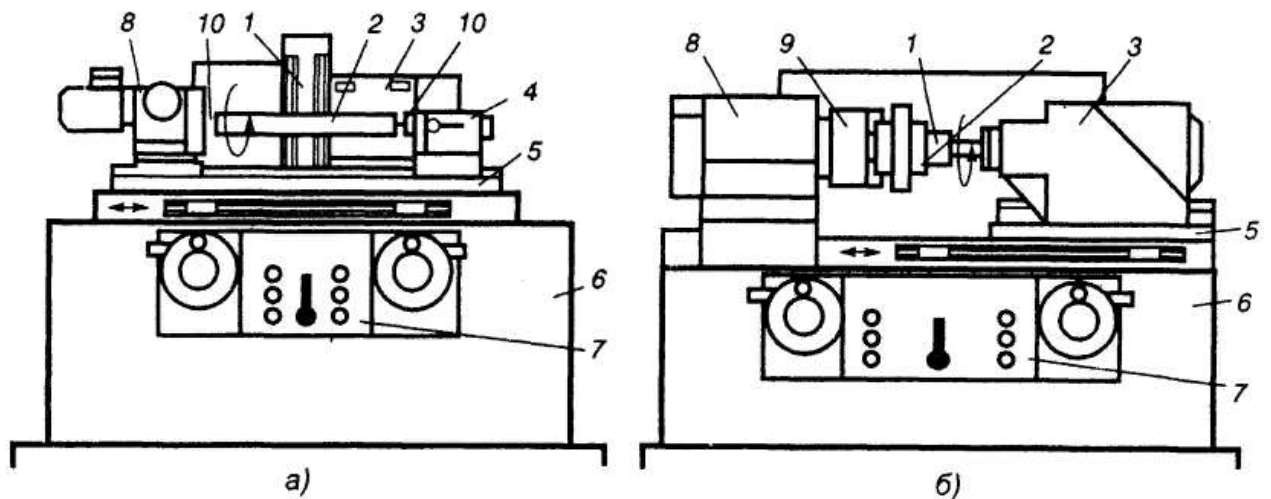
Основные узлы куглошлифовального (а) и внутришлифовального (б) станков
